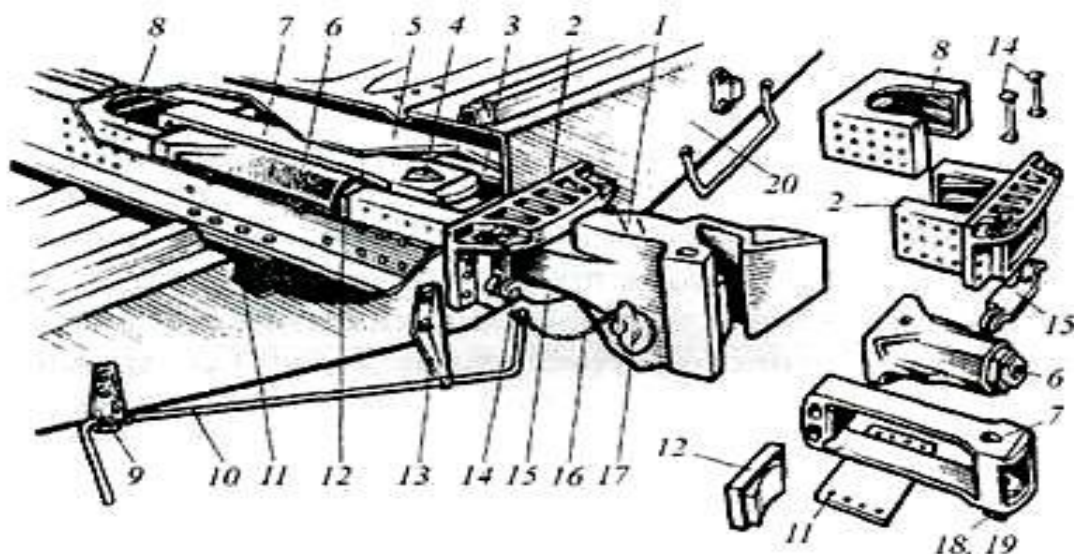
Расположение деталей автосцепного устройства вагонного типа
